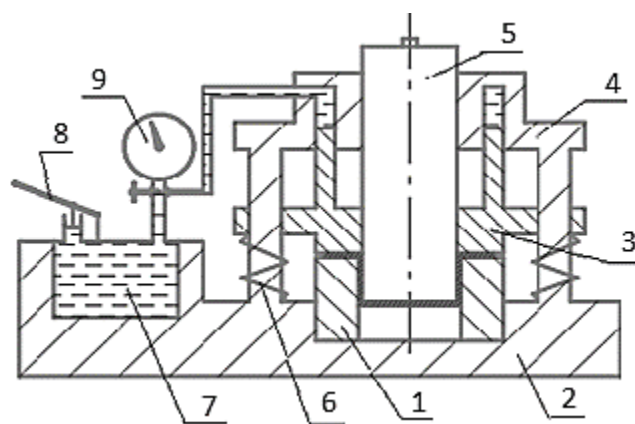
Схема штамп прибора для испытаний по Энгельгардту: 1-матрица; 2-нижняя плита; 3-прижим; 4- верхняя плита; 5-пуансон; 6-пружина возврата; 7-полость для масла; 8-ручной насос; 9-манометр.
